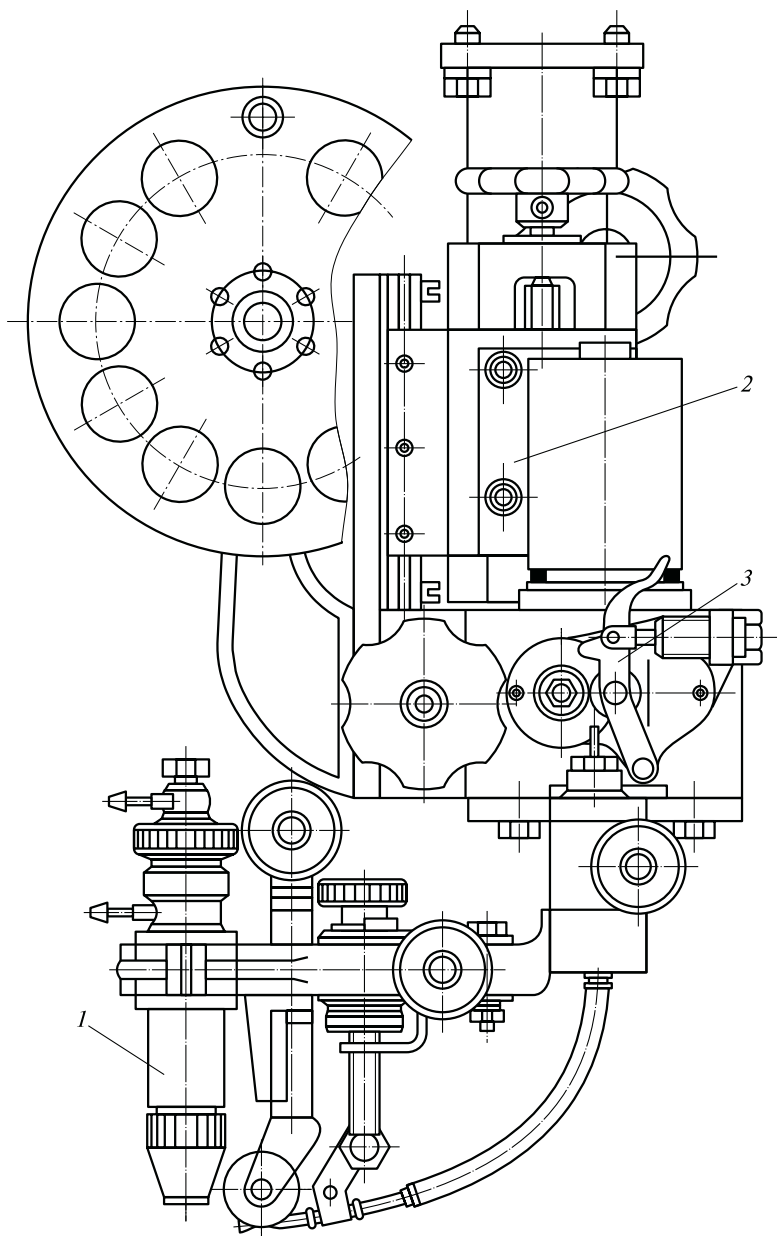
Сварочная головка для сварки вольфрамовым электродом:
